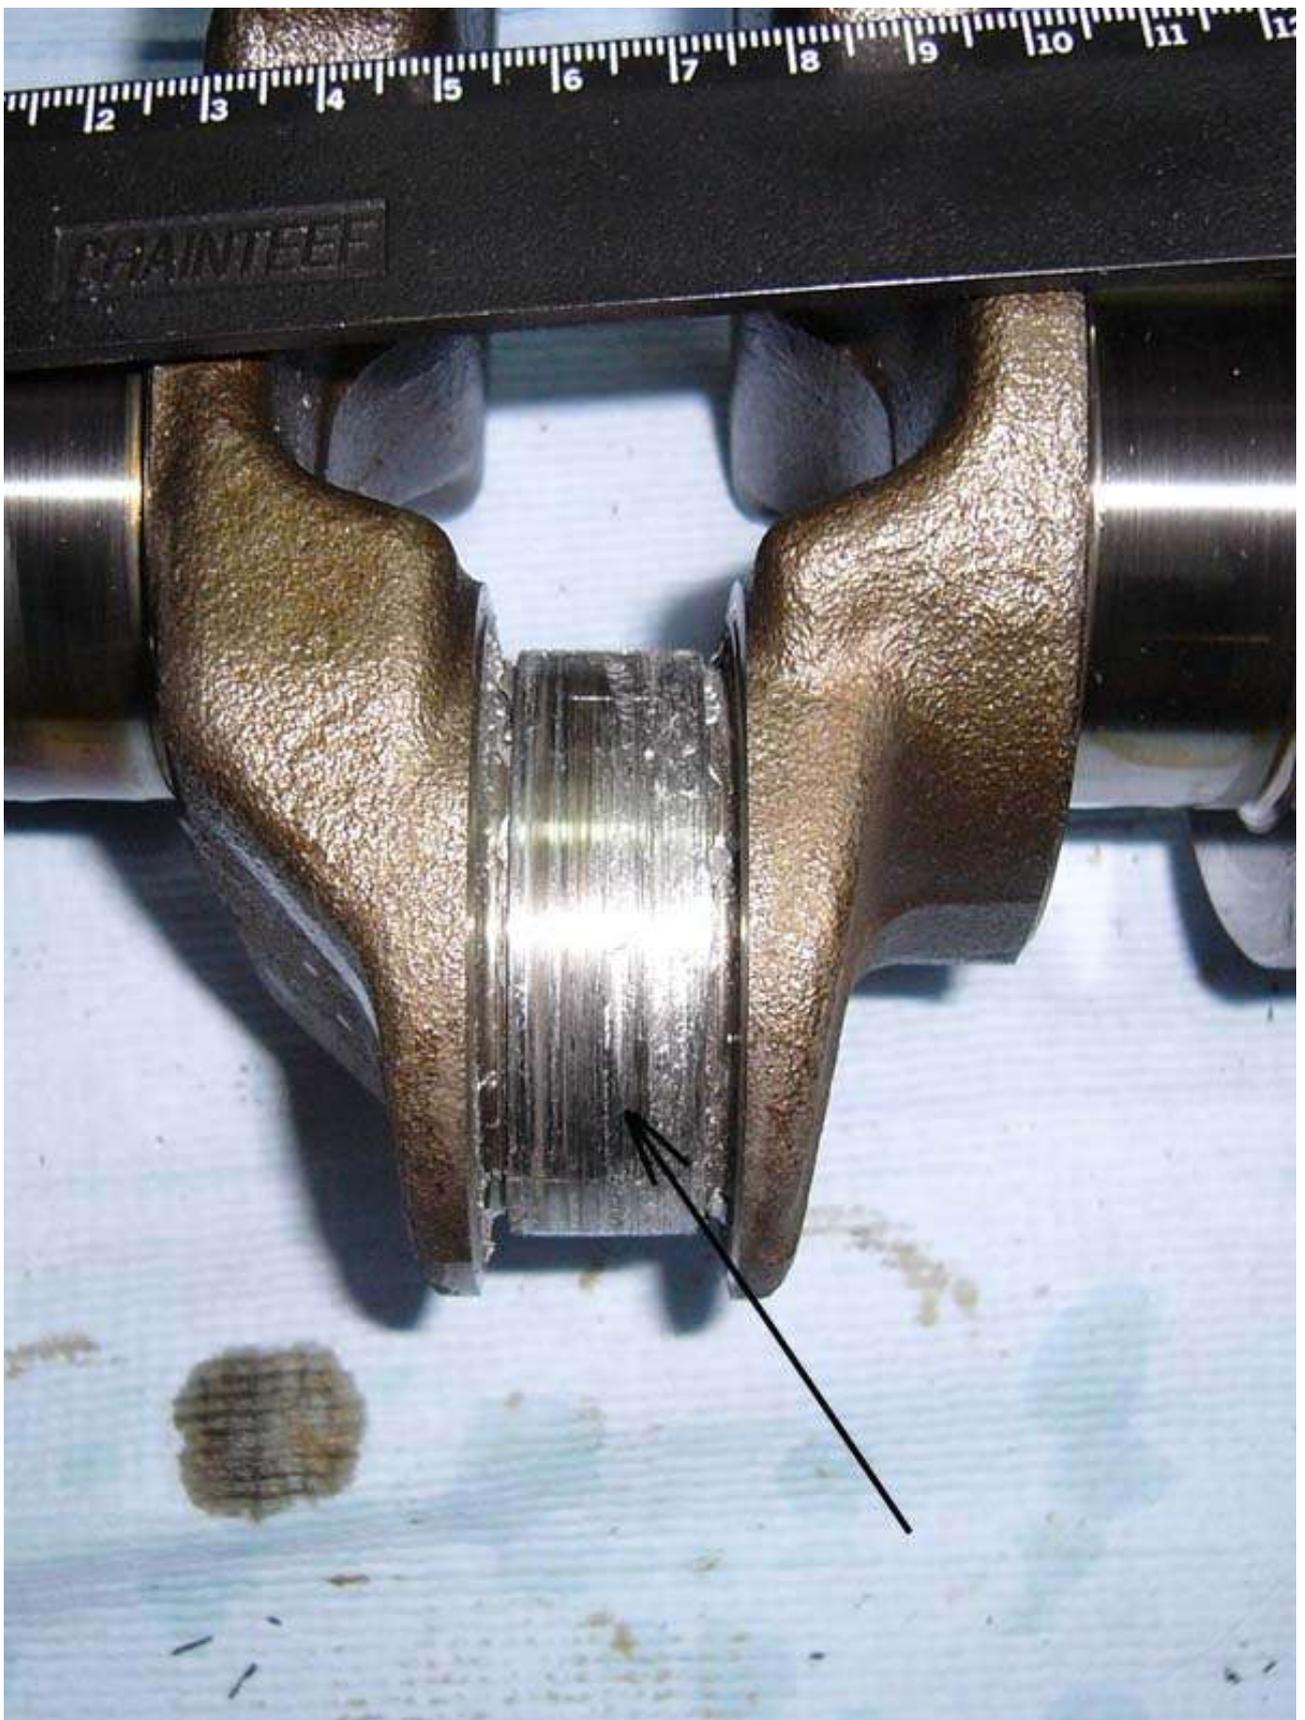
Вкладыши 2-го шатунного подшипника на шейке коленчатого вала (показаны стрелкой).
